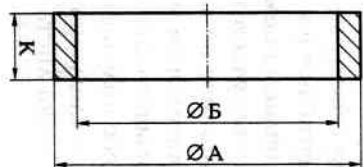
Эскиз кольцевой детали, изготавливаемой из листовой стали
